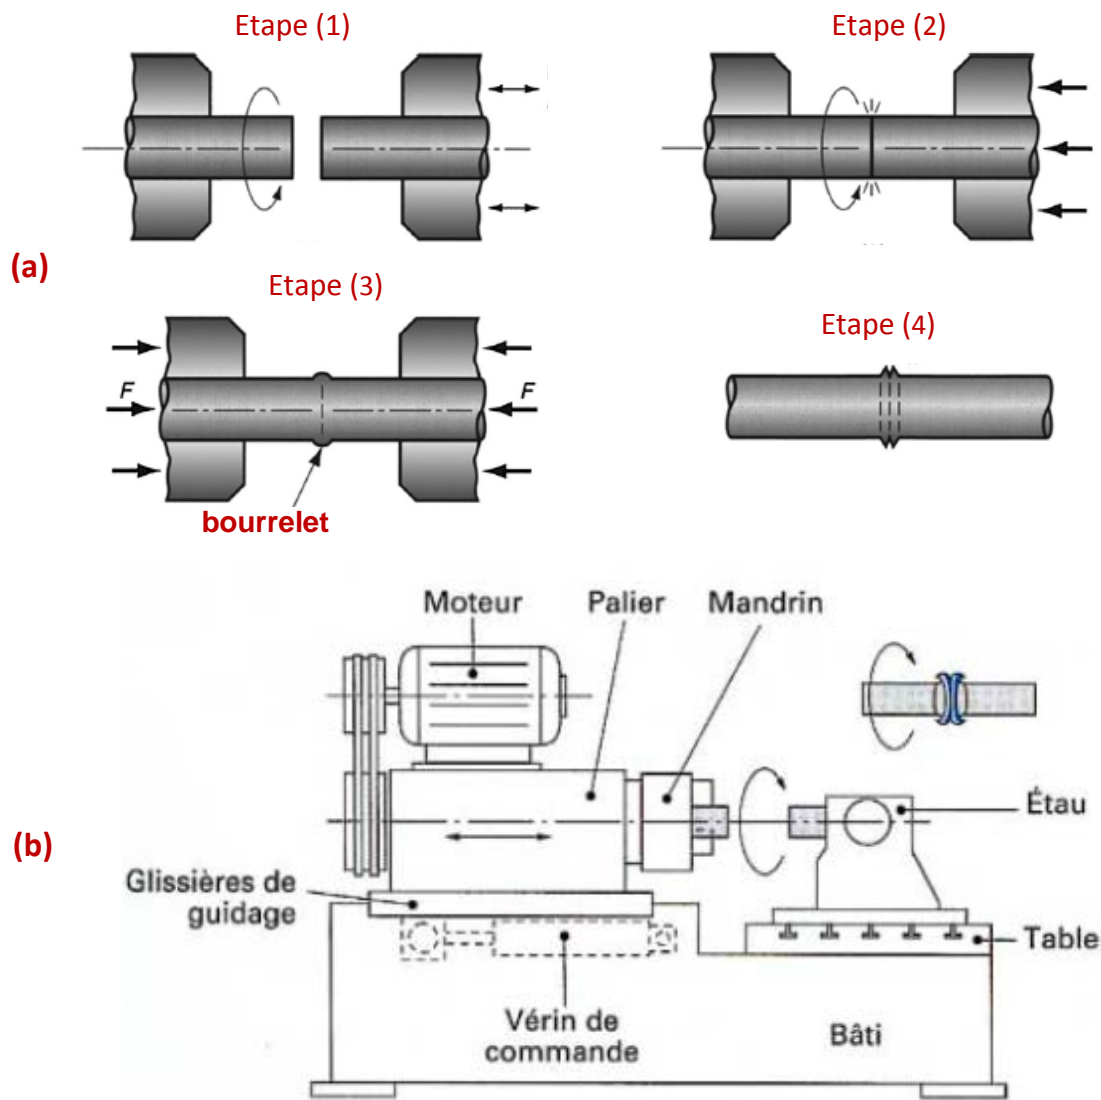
a) Principe du soudage par friction rotative [10], b) Schéma d'une machine de soudage par friction rotative [14]
